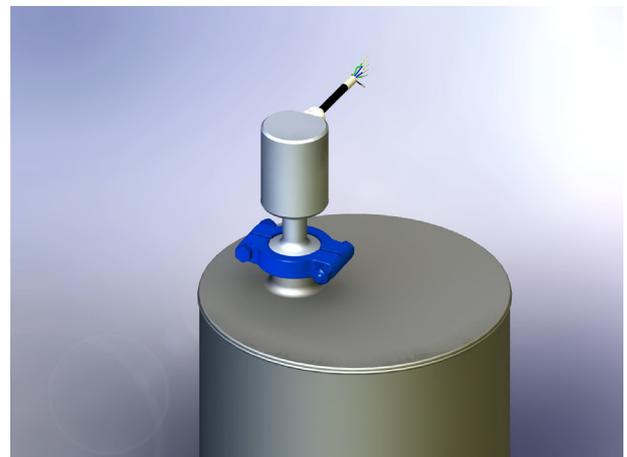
Befestigung des BTL mit 1 1/2" Tri-Clamp
